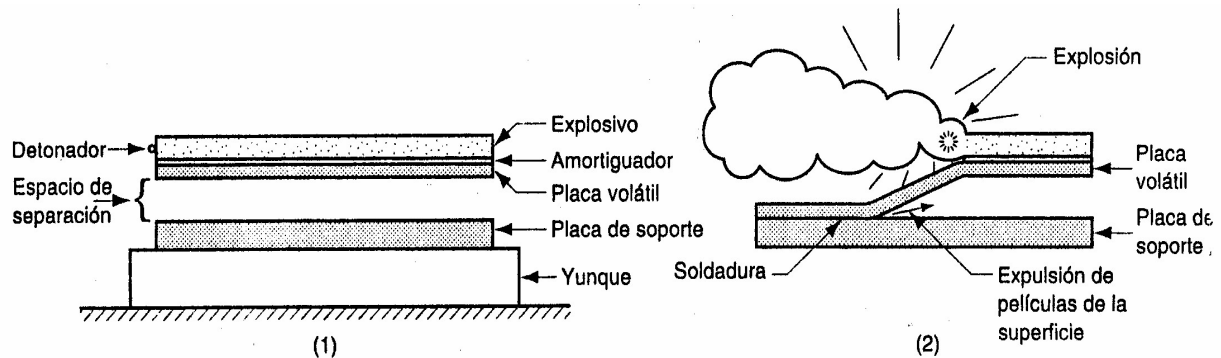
Soldadura explosiva (EXW): (1) disposición en la configuración paralela y 2) durante la detonación de la carga explosiva.
